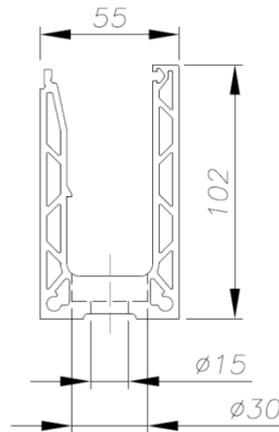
Modèle OSF – Pose sur dalle / Pose sur acrotère
